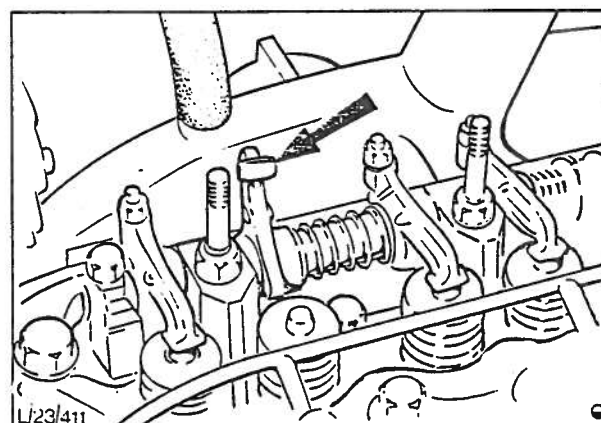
Vippearmer for fremre eksosventil frakoplet og dreid 90°.
